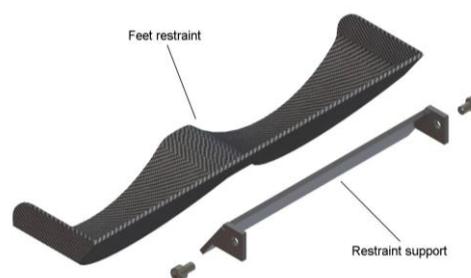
(Fuente: Robert Armengol, ETSEIB Motorsport)
